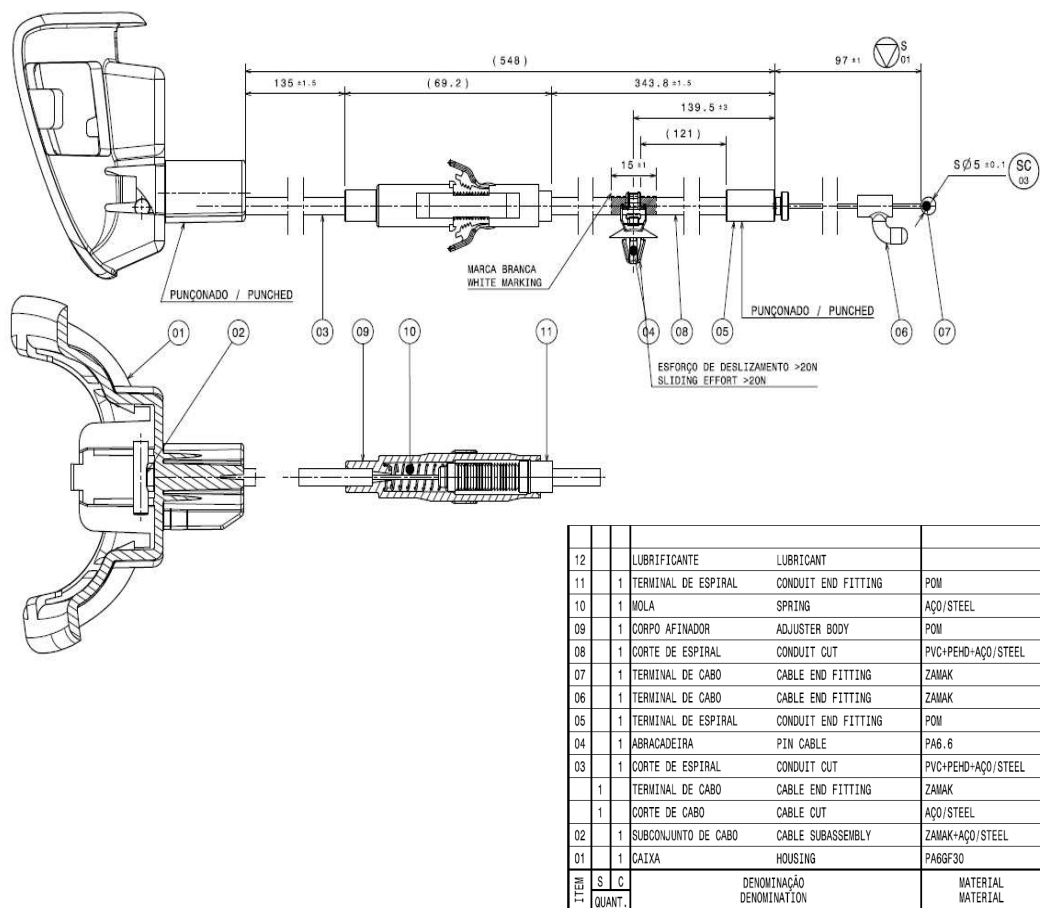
Desenho técnico do cabo de comando do assento, com a ref. 121 912 306
